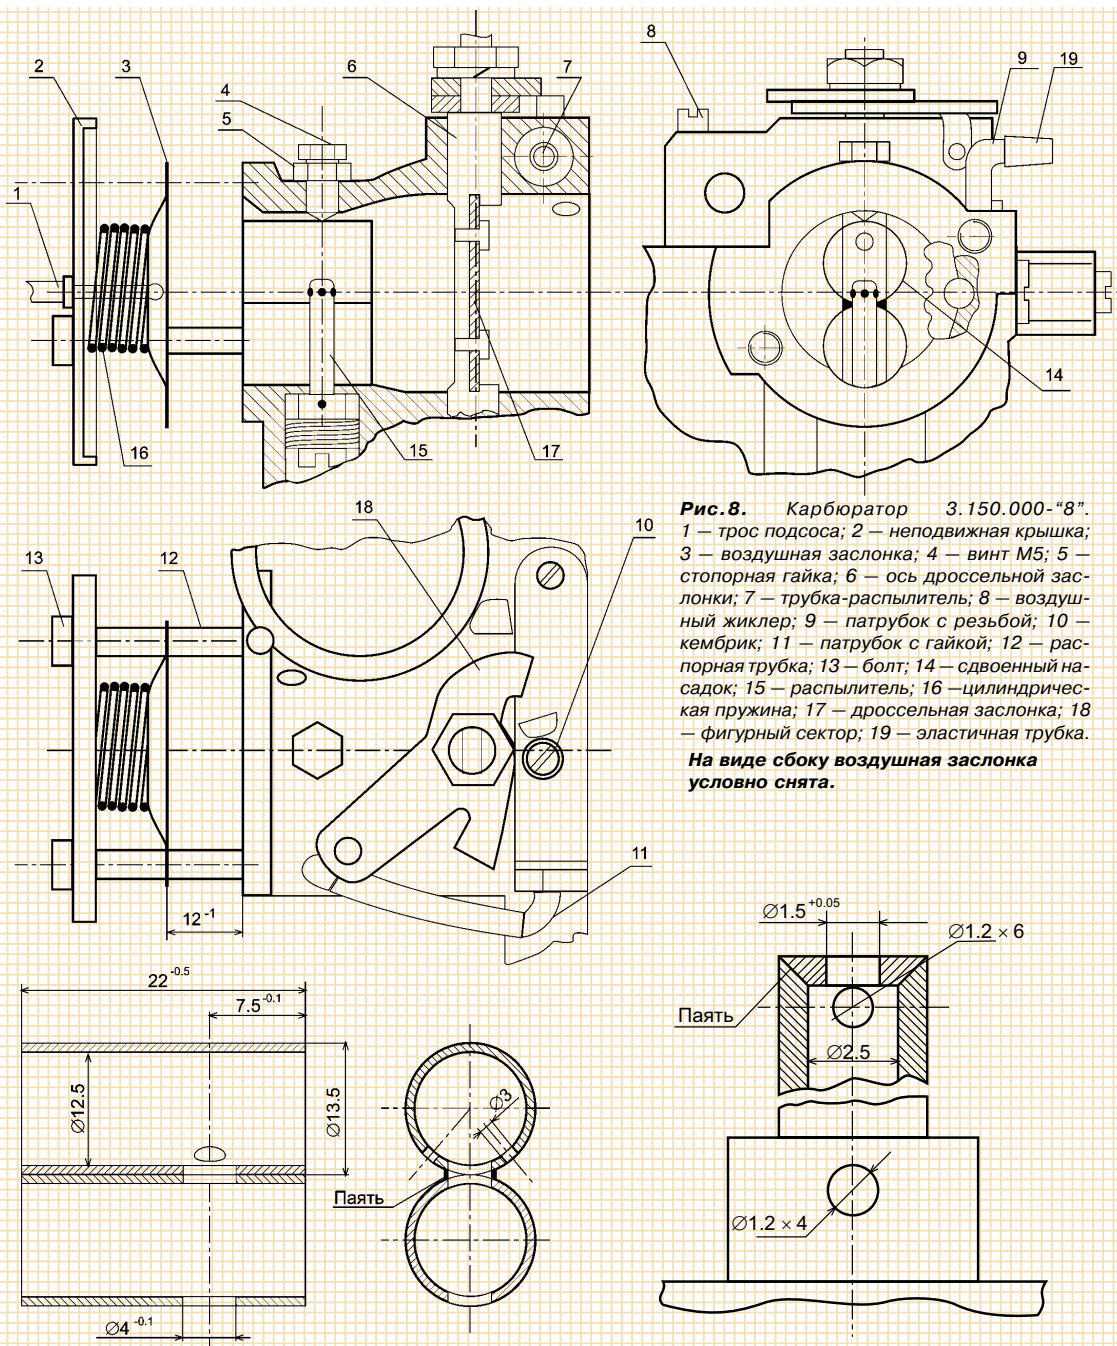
Карбюратор 3.150.000-“8”. 1 — трос подсоса; 2 — неподвижная крышка; 3 — воздушная заслонка; 4 — винт М5; 5 — стопорная гайка; 6 — ось дроссельной заслонки; 7 — трубка-распылитель; 8 — воздушный жиклер; 9 — патрубок с резьбой; 10 — кембрик; 11 — патрубок с гайкой; 12 — распорная трубка; 13 — болт; 14 — двойной насадок; 15 — распылитель; 16 — цилиндрическая пружина; 17 — дроссельная заслонка; 18 — фигурный сектор; 19 — эластичная трубка.
